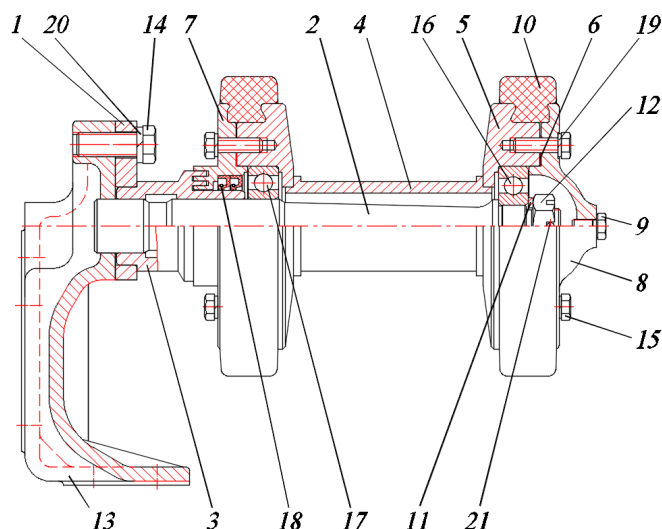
Конструктивная схема поддерживающего катка с кронштейном:
